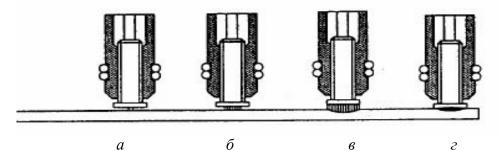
Стадии сварки «усов» конденсаторным разрядом
